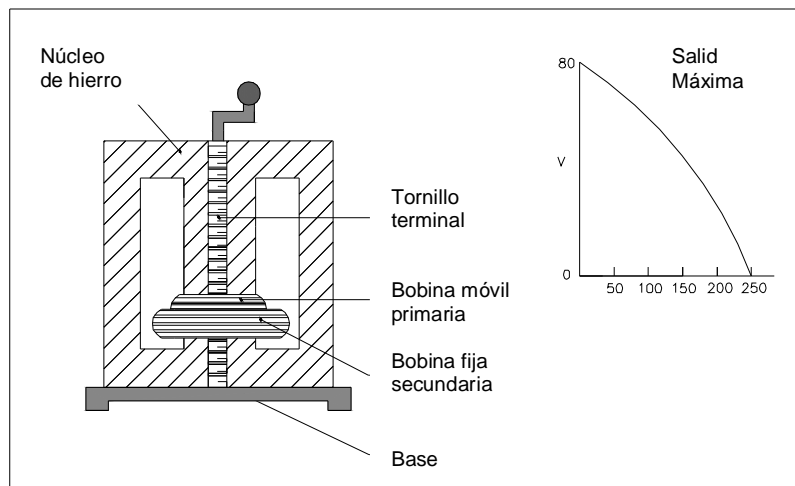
b). - Transformador de CA con bobinas lo mas juntas posible (AMERICAN WELDING SOCIETY, Manual de soldadura, Tomo I, Pág. 20)
